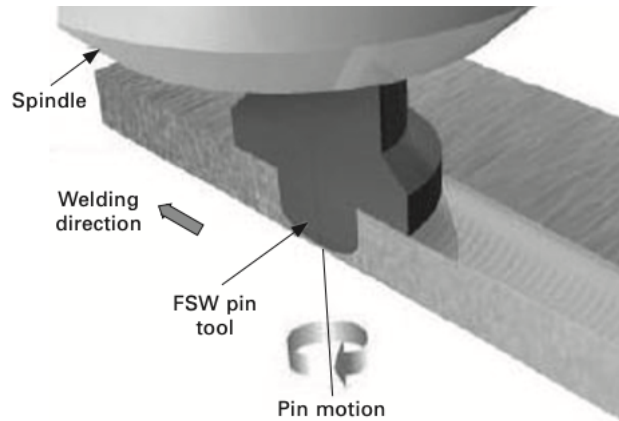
Sección de la herramienta FSW con pasador fijo. [9]
